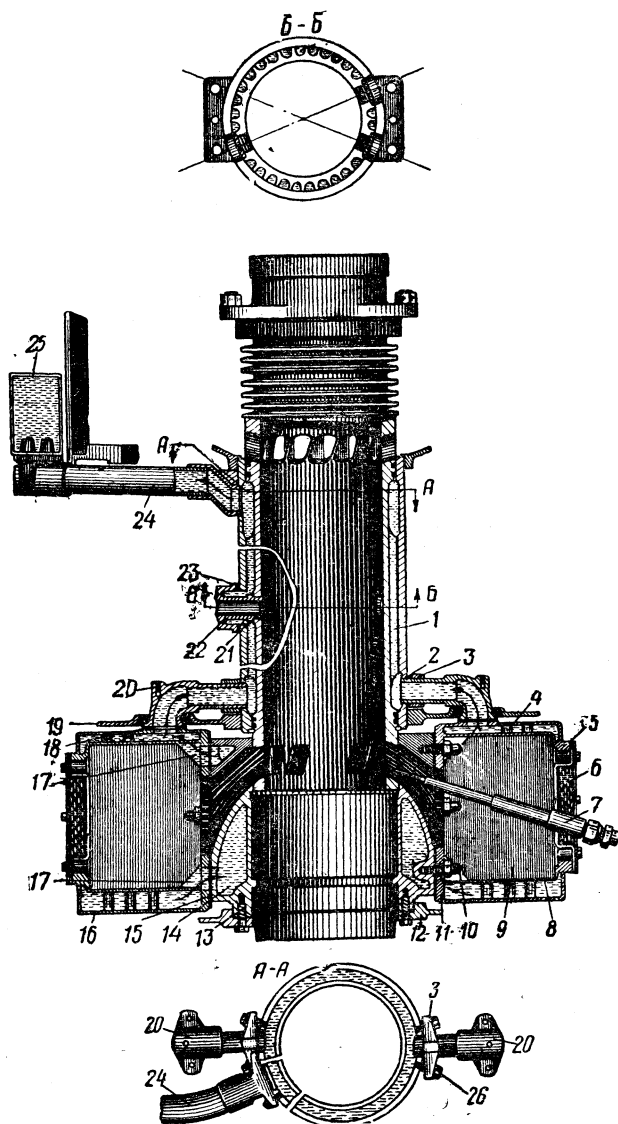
Выпускные коллекторы, коробка и охлаждение цилиндровой гильзы дизеля 2Д100:
